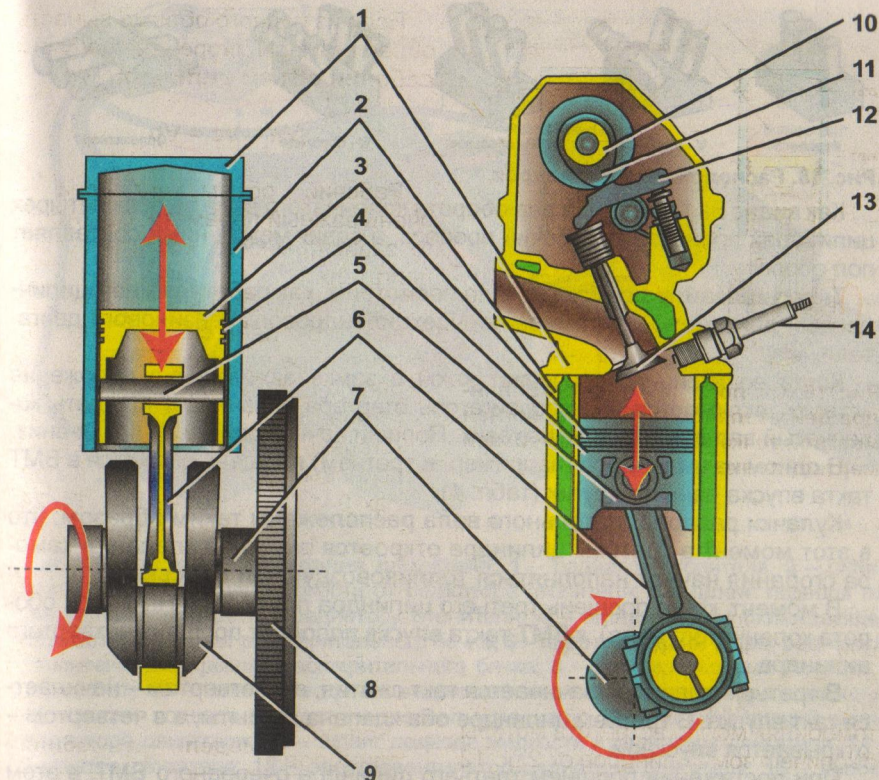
Одноцилиндровый бензиновый двигатель внутреннего сгорания: 1 — головка цилиндра; 2 — цилиндр; 3 — поршень; 4 — поршневые кольца; 5 — поршневой палец; 6 — шатун; 7 — коленчатый вал; 8 — маховик; 9 — кривошип; 10 — распределительный вал; 11 — кулачок распределительного вала; 12 — рычаг; 13 — впускной клапан; 14 — свеча зажигания
